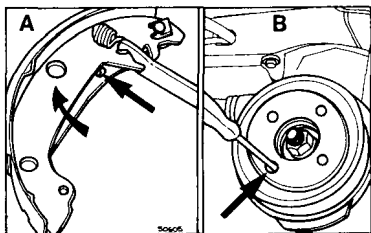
Выведение рычага привода стояночного (ручного) тормоза из зацепления
